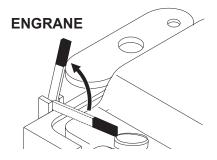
Palanca de transmisión engrane/desengrane (posición de engrane)
